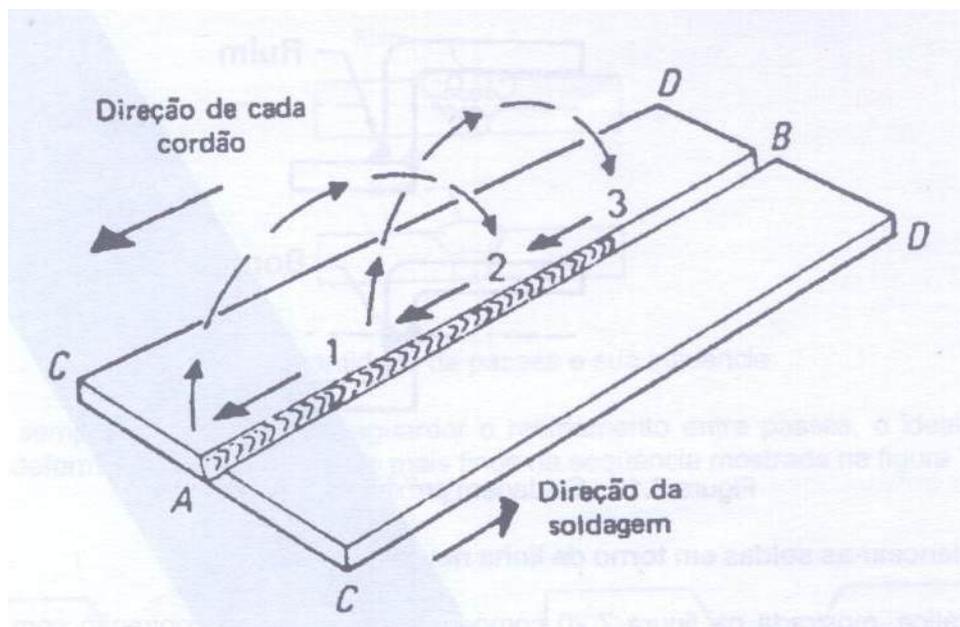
Soldagem com passe a ré (“backstep welding”)
